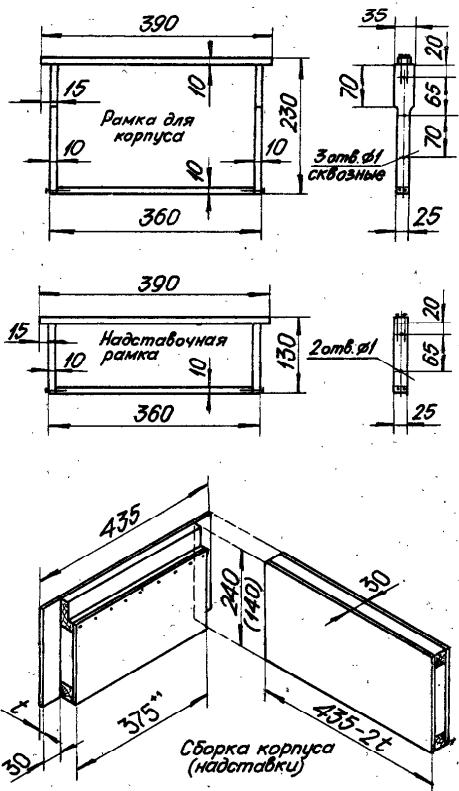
Схема сборки корпуса, рамки для корпуса и надставочной рамки улья типа «Стандарт Островской».
